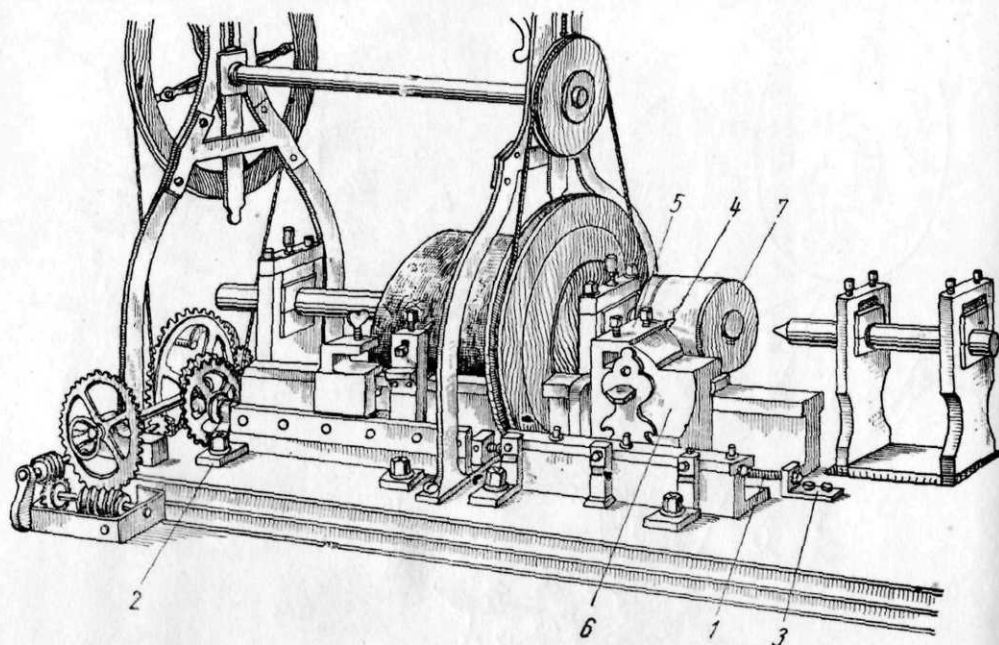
Кинематическая схема большого токарно-копировального станка Нартова 1718—1729 гг.
